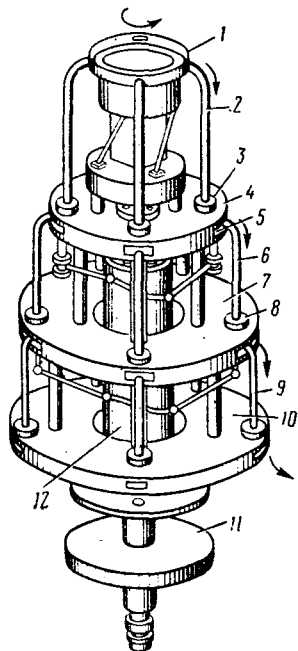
Принципиальная схема многоярусного роторного станка для сборки
